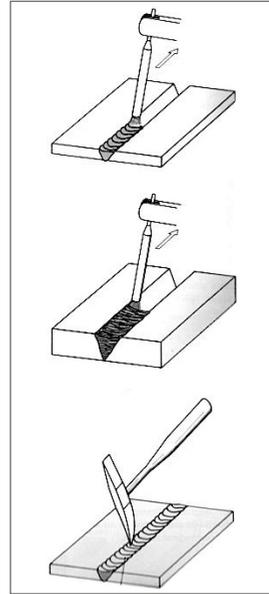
Tätigkeitsabfolgen beim Schweißen
